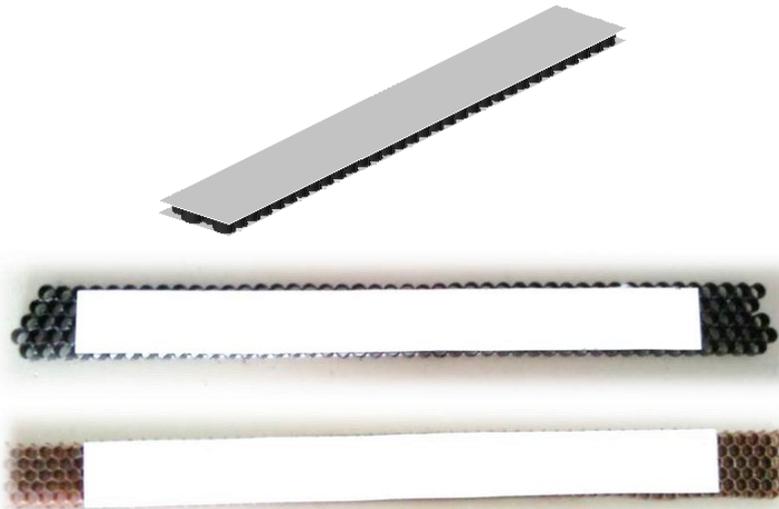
Esquema (imagen superior) y fotografías de probetas con núcleo alternativo (imagen intermedia) y original (imagen inferior).
